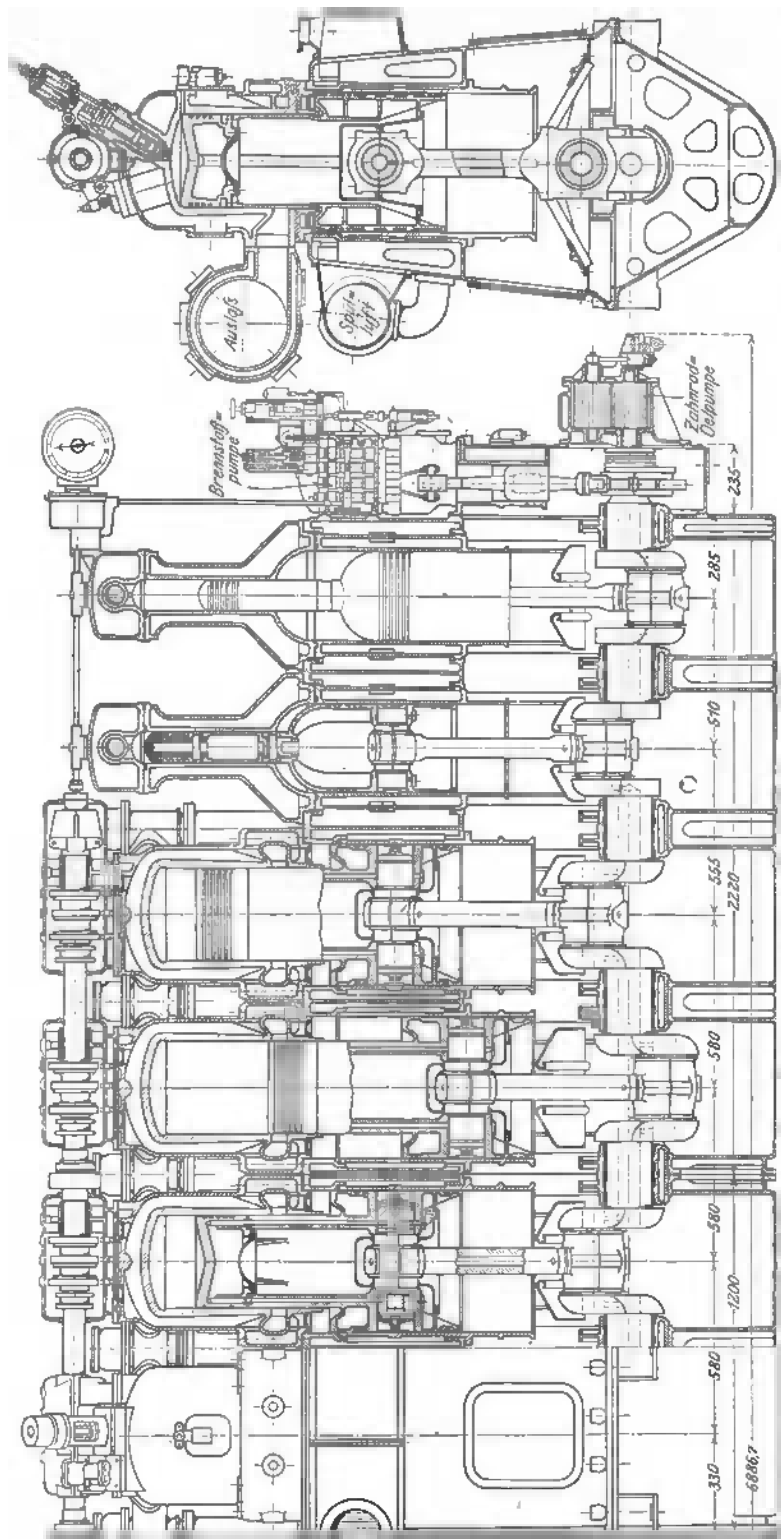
121. Achtzylindrige Unterseeboots-Ölmaschine, 900 PSe.
